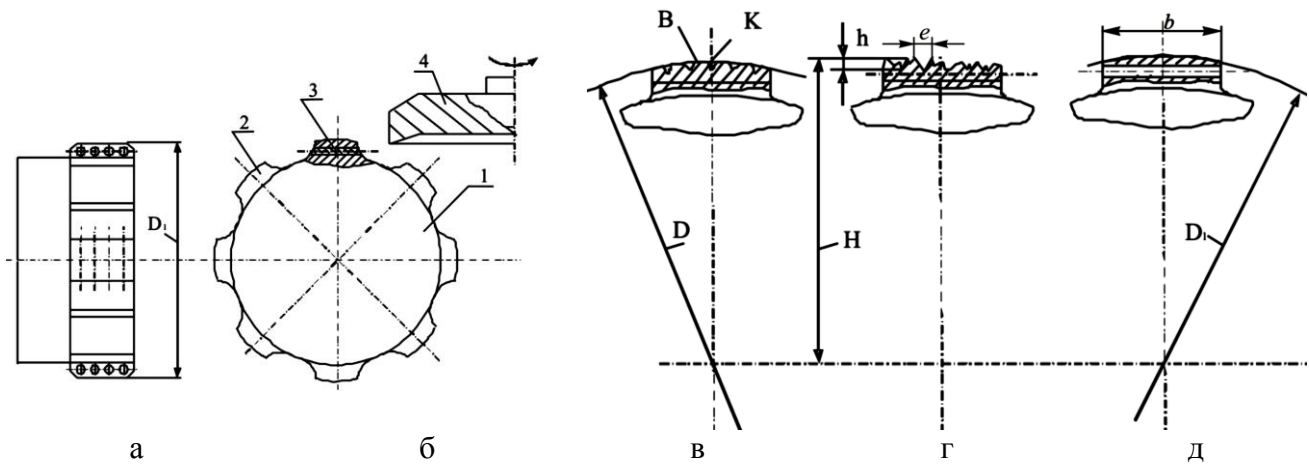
Запропонована конструкція радіального підшипника ковзання: а – вигляд заготовки вала; б – вигляд збоку вала та дисковий інструмент для обробки опорних елементів; в – перетин заготовки опорного елемента із бронзовими стрижнями; г – хвиляста поверхня, одержана в результаті ТФО; д – поверхня опорного елемента, одержана в результаті комплексної обробки
